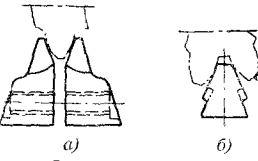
Схема нарезания цилиндрических колес червячной фрезой.
